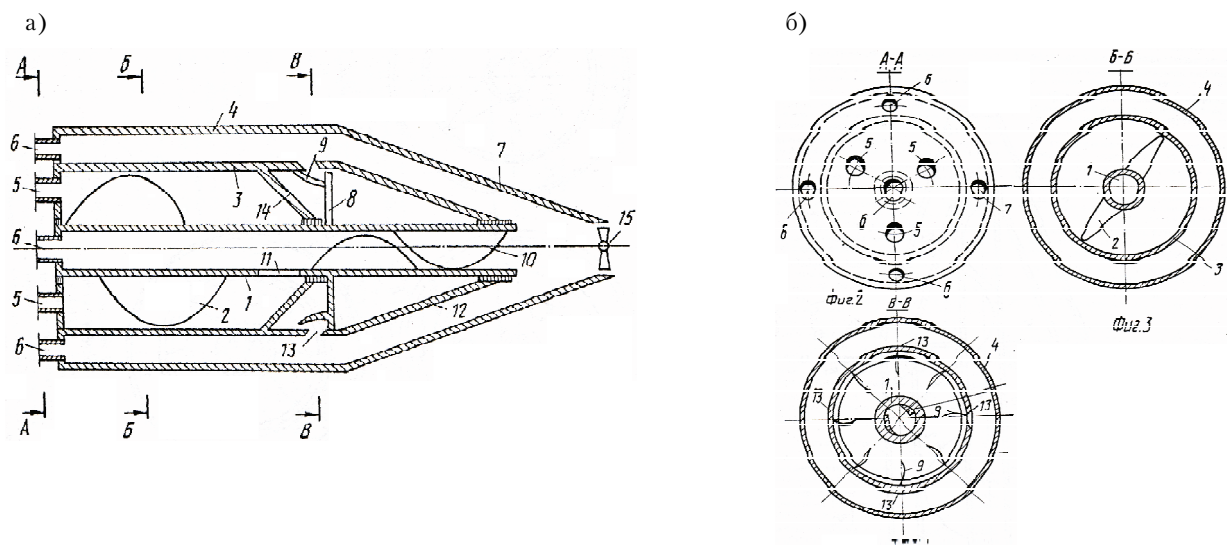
Устройство (сопло) а) продольный и б) поперечный разрезы, для набрызга текучей смеси: 1 – полый вал, 2 – перемешивающие элементы, 3 – внутренний цилиндрический корпус, 4 – наружный цилиндрический корпус, 5 – соединительные источники текучей смеси, 6 – соединительные источники сжатого воздуха, 7 – наружное сопло, 8 – диск, 9 – криволинейные лопасти, 10 – винтовая спираль, 11 – перепускные окна, 12 – внутреннее сопло, 13 – отверстие, 14 – перегородка в виде усеченного конуса, 15 – заслонка.
